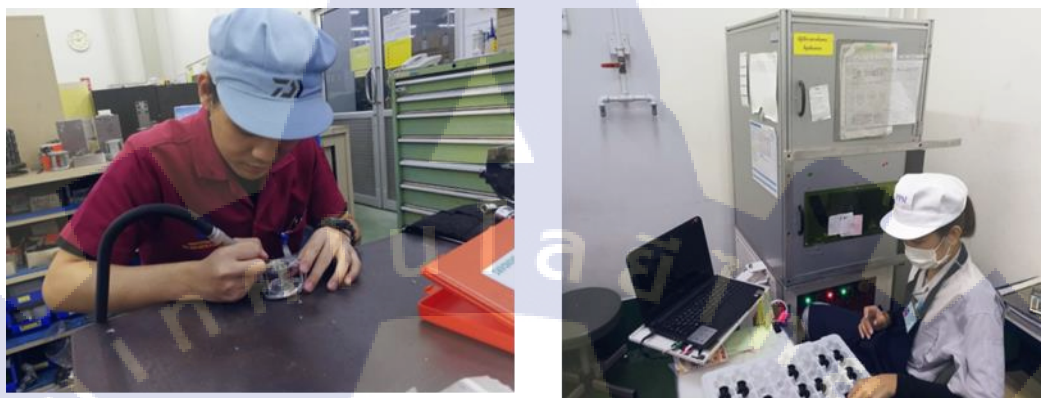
รวบรวม PART จากแผนก MACHINE
